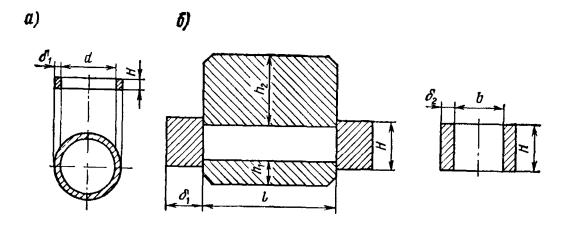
Формы для изготовления и уплотнения образцов: а — для изготовления высохших образцов — таблеток; б — для уплотнения образцов — балочек
